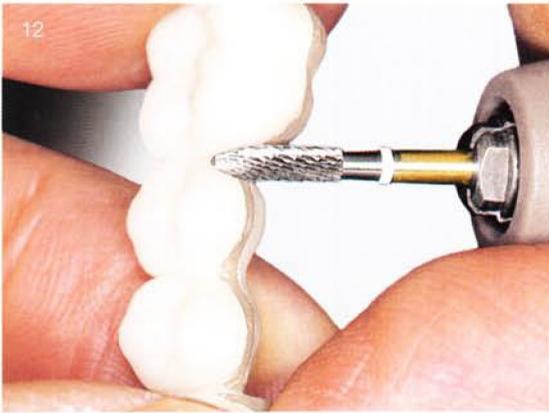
Mit dem UK-Fräser hat Komet ein Werkzeug geschaffen, das sich gleichermaßen für Keramik und Komposit wie für Metalle eignet
